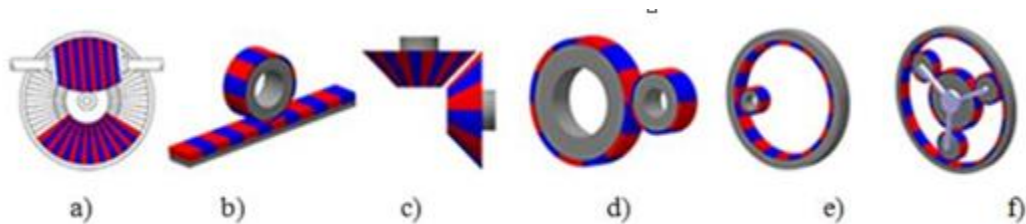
Engranaje magnético convertidos: a) Engranaje magnético de tornillo b) Engranaje de cremallera y piñón c) Engranaje magnético cónico d) Engranaje magnético cilíndrico externo e) Engranaje recto interno f) Engranaje magnético planetario.
